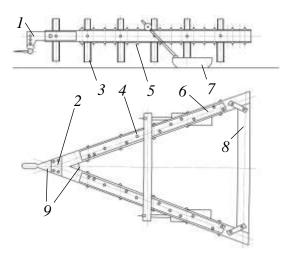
Корчевальная борона К-1: I – прицепное устройство; 2 – накладки, скрепляющие переднюю часть рамы; 3 – зуб; 4 – боковые брусья; 5 – нижние полосы оковки; 6 – верхние полозки; 6 – задний брус; 9 – скобы
